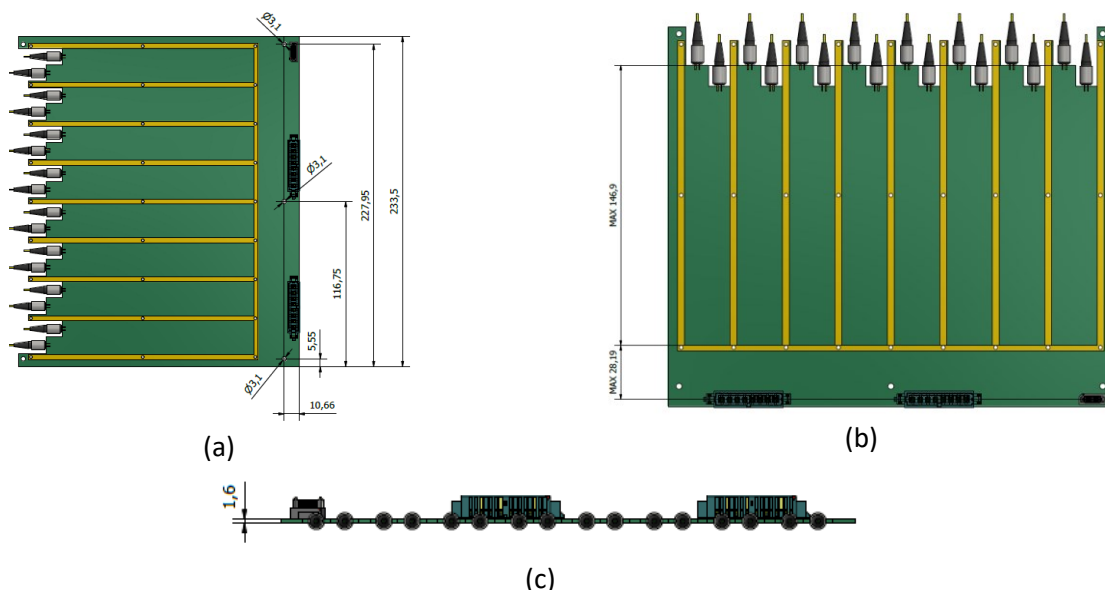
Dimensioni meccaniche PCB PREADU: (a) larghezza scheda e posizione fori interfaccia con scheda ADU, (b) dimensioni massime ingombri PCB e (c) spessore PCB.
